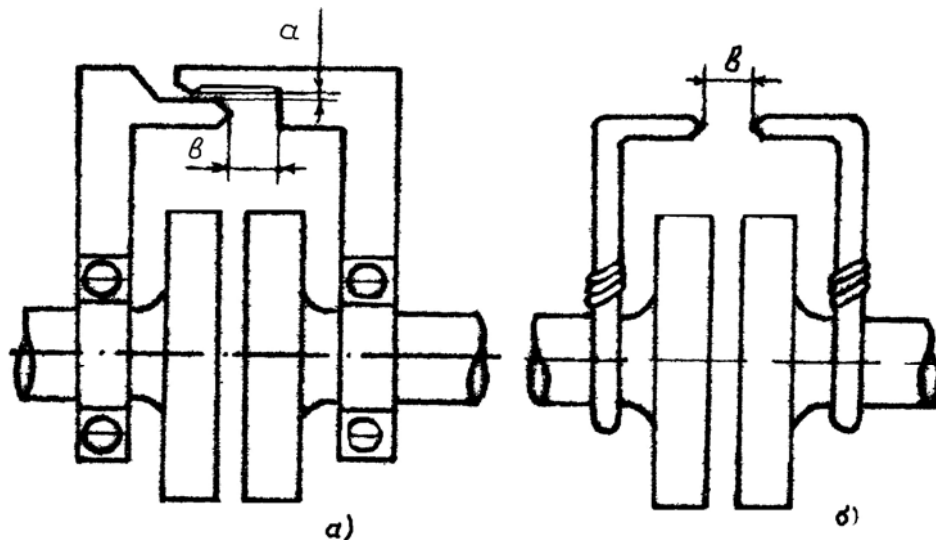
Выверка установки электродвигателя и рабочей машины, соединенных муфтой:
